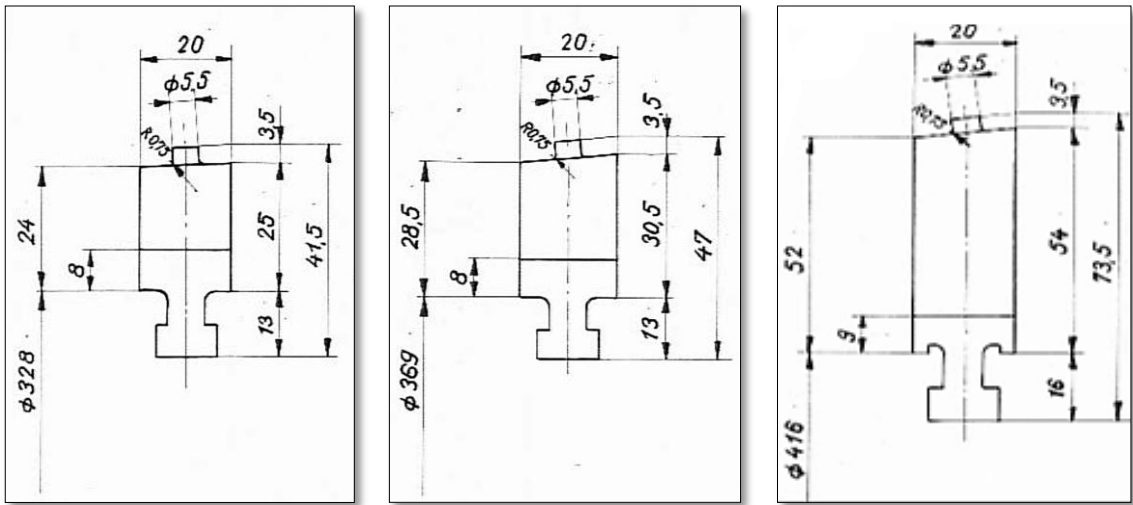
dimensioni principali delle pale del 2°, 5° e 9° stadio della macchina n° 1, in ordine partendo da sinistra.
